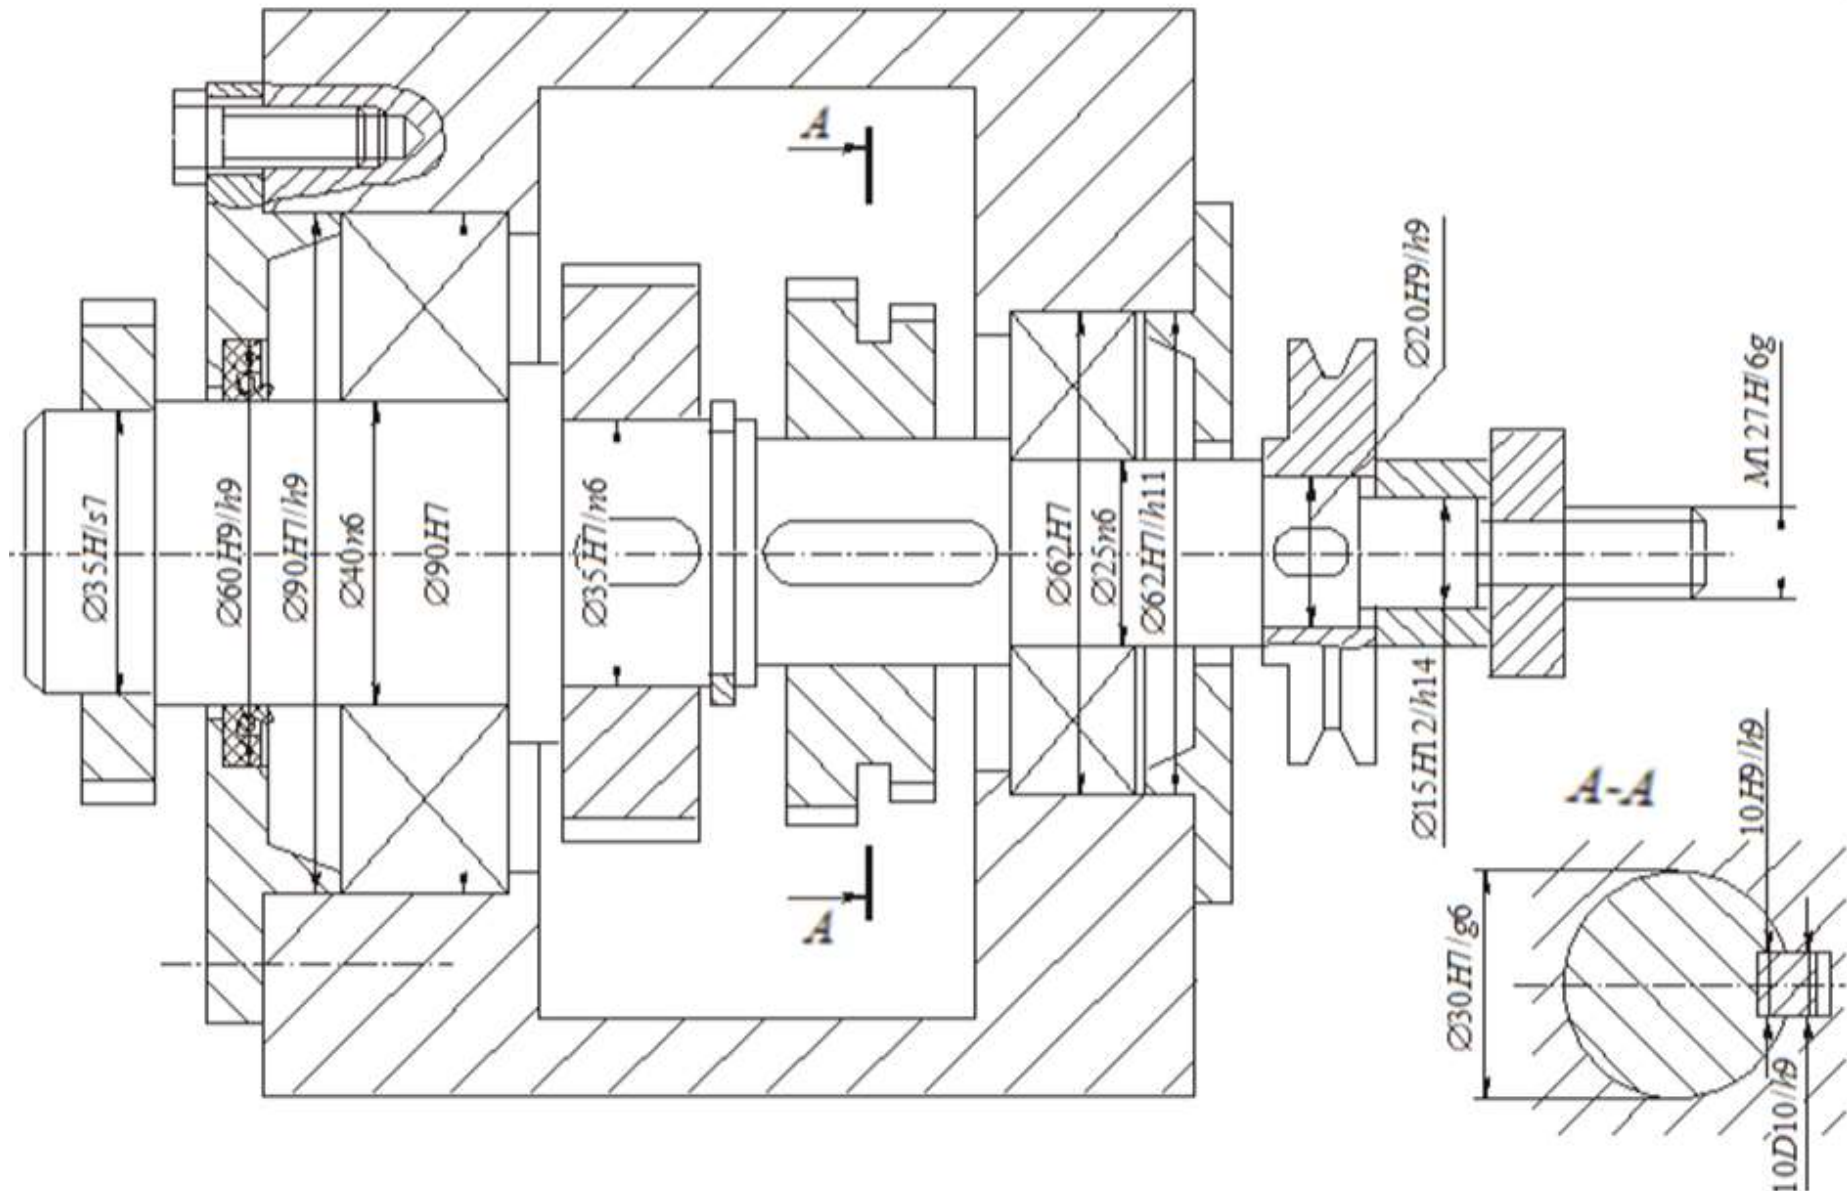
Пример сборочного чертежа (эскиза) редуктора
